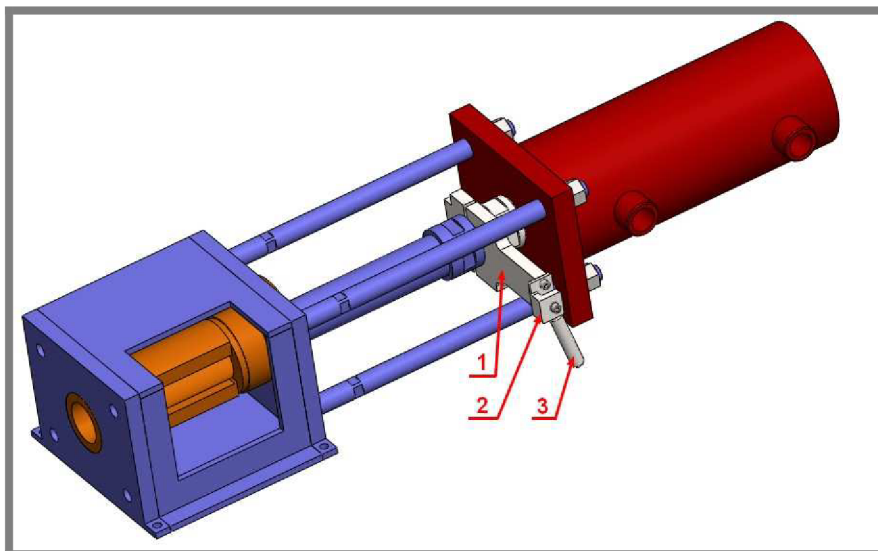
Řez prohrnovacího a otočného mechanismu
